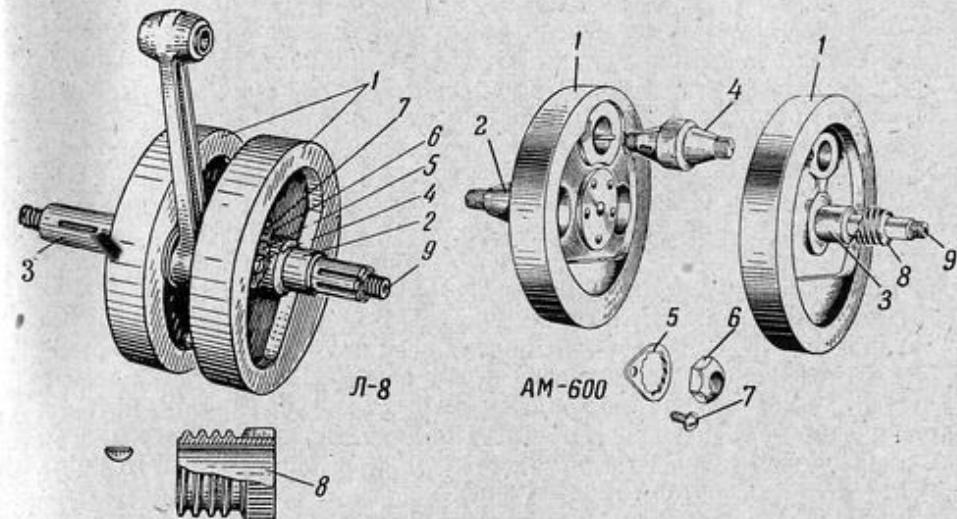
Разборные коленчатые валы двигателей Л-8 и АМ-600:
